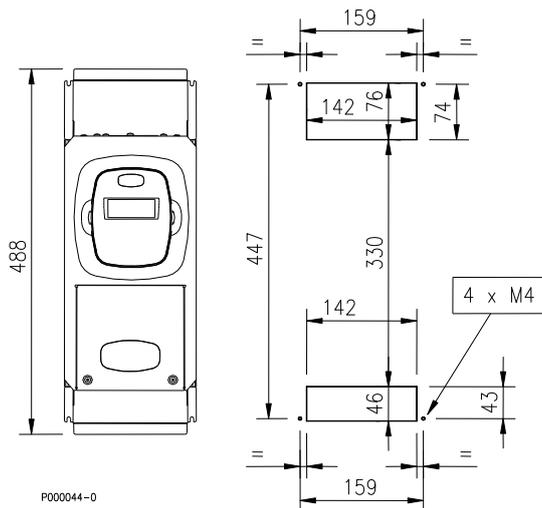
Dime di foratura del pannello per montaggio passante IRIS BLUE S05
